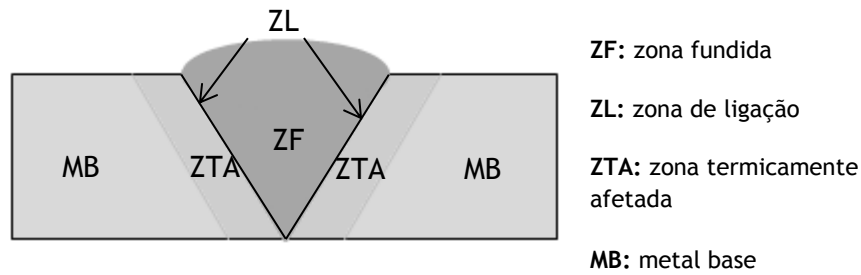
Zonas constituintes de uma junta em V após soldadura
